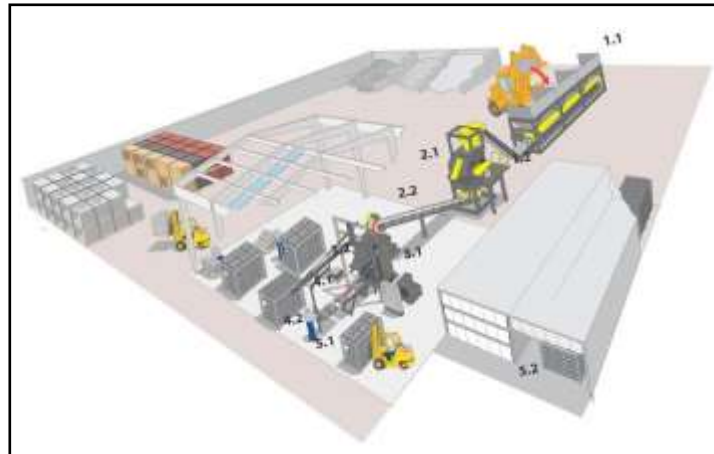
Esquema Layout de la planta de prefabricados de concreto
